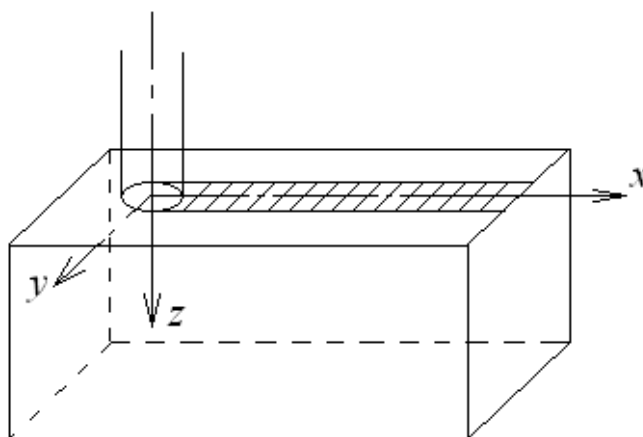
Схема движения лазерного луча вдоль образца ВК6
